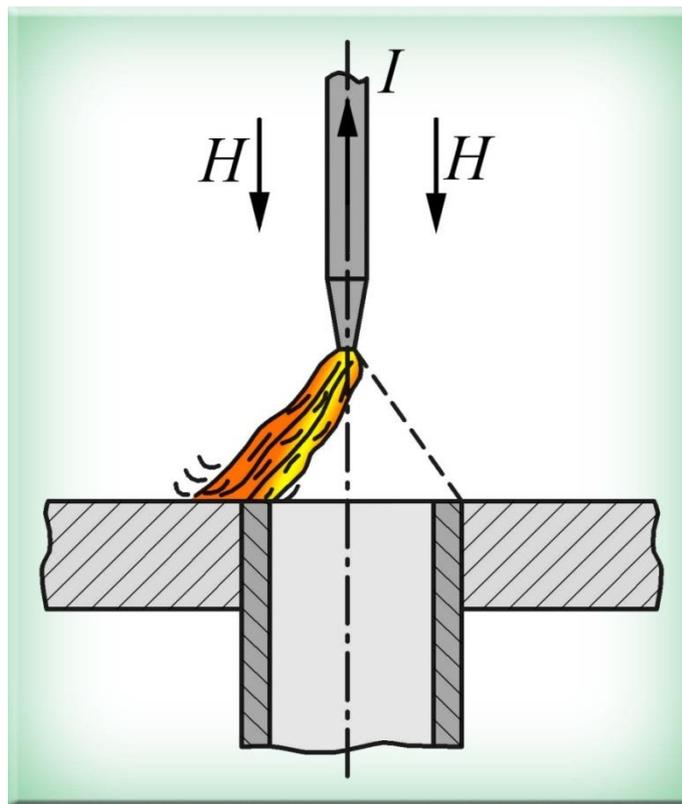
Схема сварки трубы в трубную доску вращающейся «конусной» дугой
